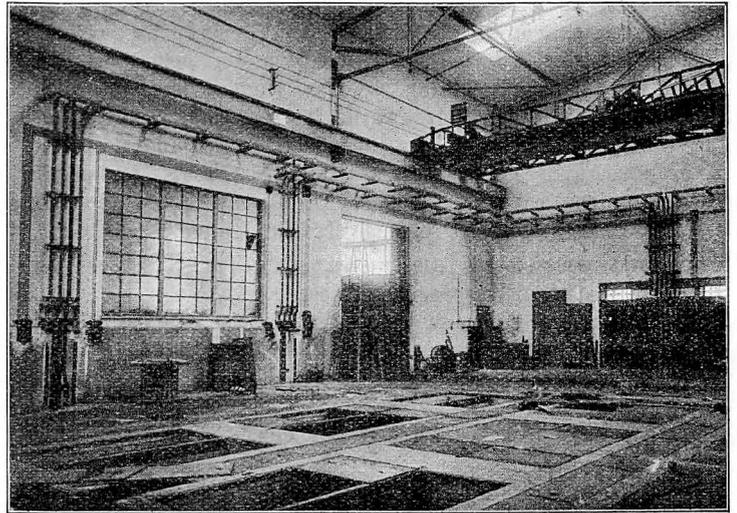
Ansicht der Schweißleitungen von der Schalttafel zu den Schweißplätzen.
